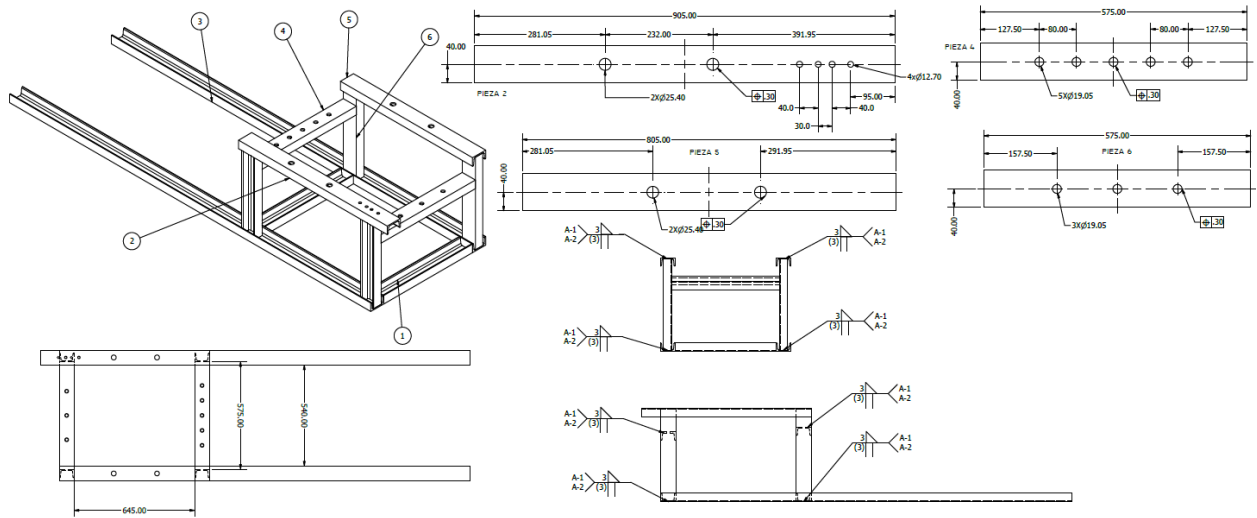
Plano de ensamble soldado: Estructura. Detalle de componentes.
